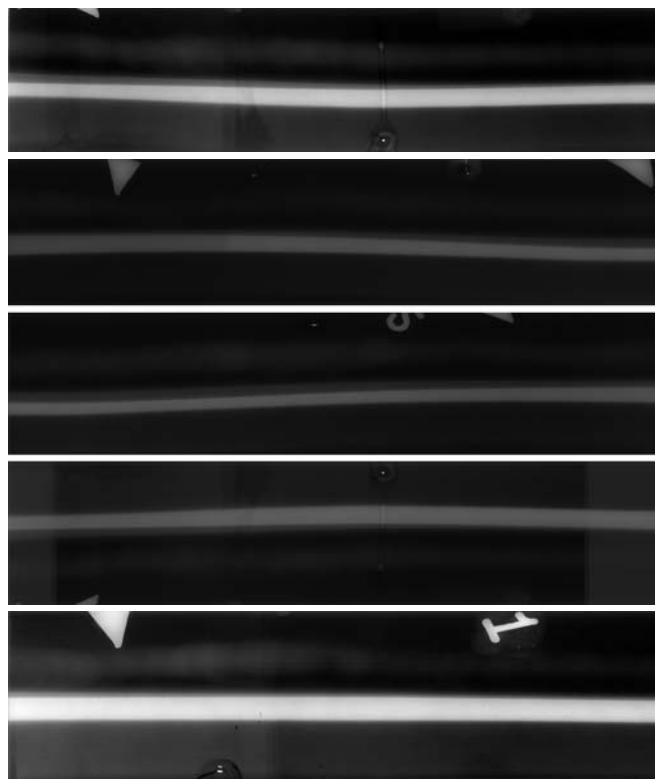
Рентгеновский снимок по длине кольцевого шва алюминиевой корпусной детали (масштаб 3:1)
